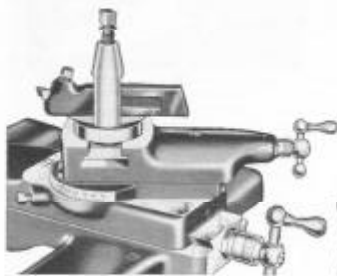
Soporte compuesto colocado a un ángulo para torneado cónico
